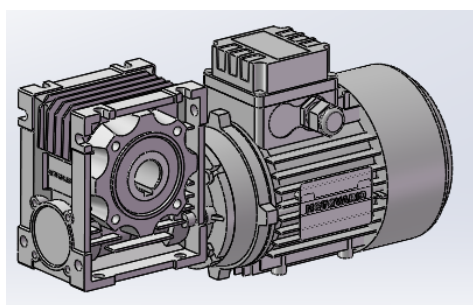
Motorreductor Motovario con reductora de tornillo sinfín.
